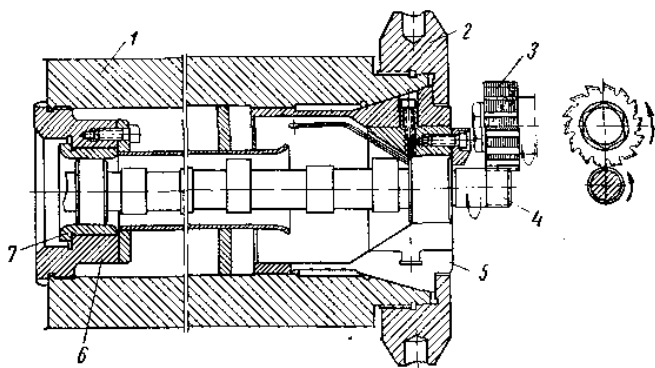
Наладка резьбофрезерного станка с зажимом заготовки в специальном патроне:
